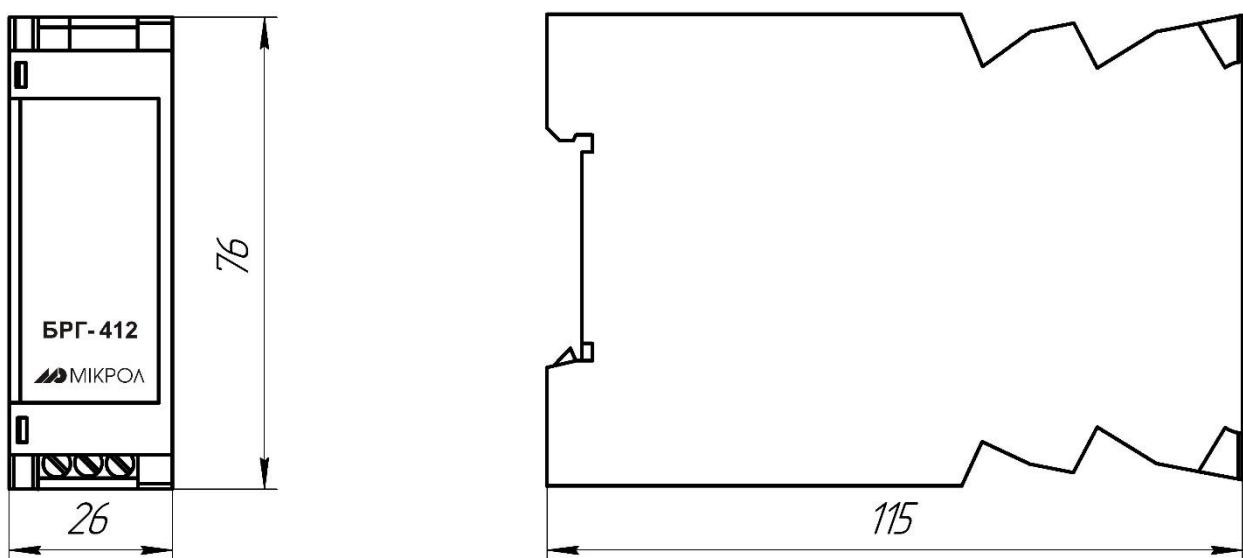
Зовнішній вигляд та габаритні розміри БРГ-422
